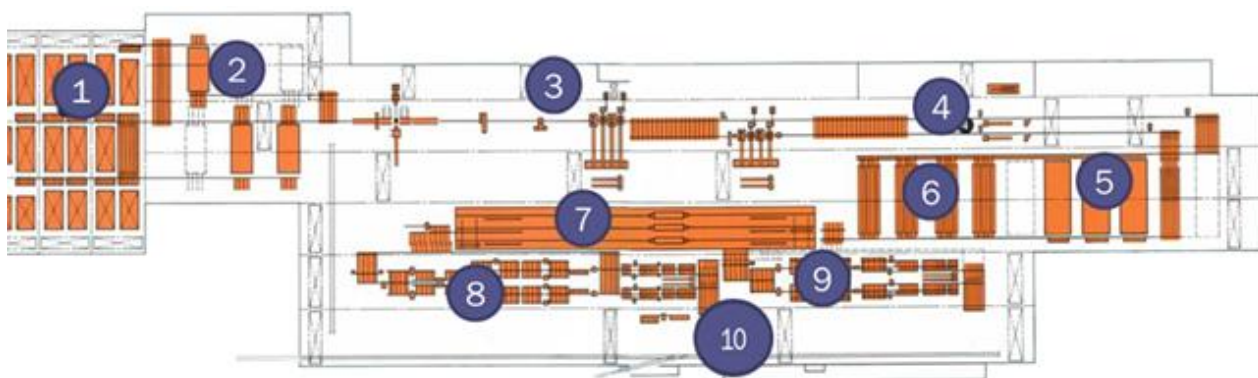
Схема компоновки агрегатов заготовочного стана 700:
